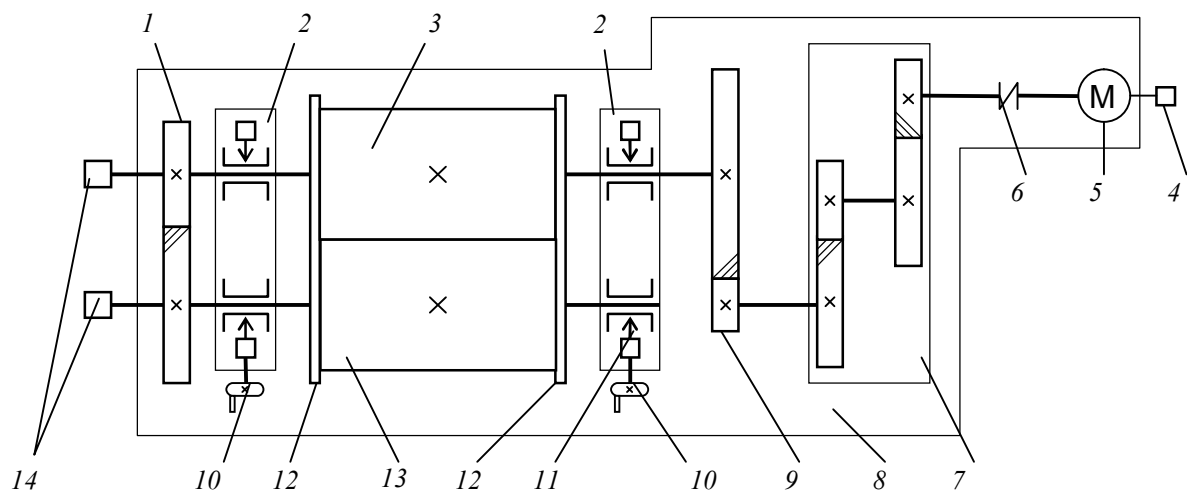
Схема валкової установки: 1 – фрикційні шестерні; 2 – станини; 3 – задній валок; 4 – тахогенератор; 5 – приводний електродвигун; 6 – муфта; 7 – редуктор; 8 – зварна основа; 9 – приводна зубчаста передача; 10 – механізми переміщення переднього валка; 11 – месдози; 12 – обмежувальні стріли; 13 – передній валок; 14 – колектори підведення електричного струму до нагрівників валка
